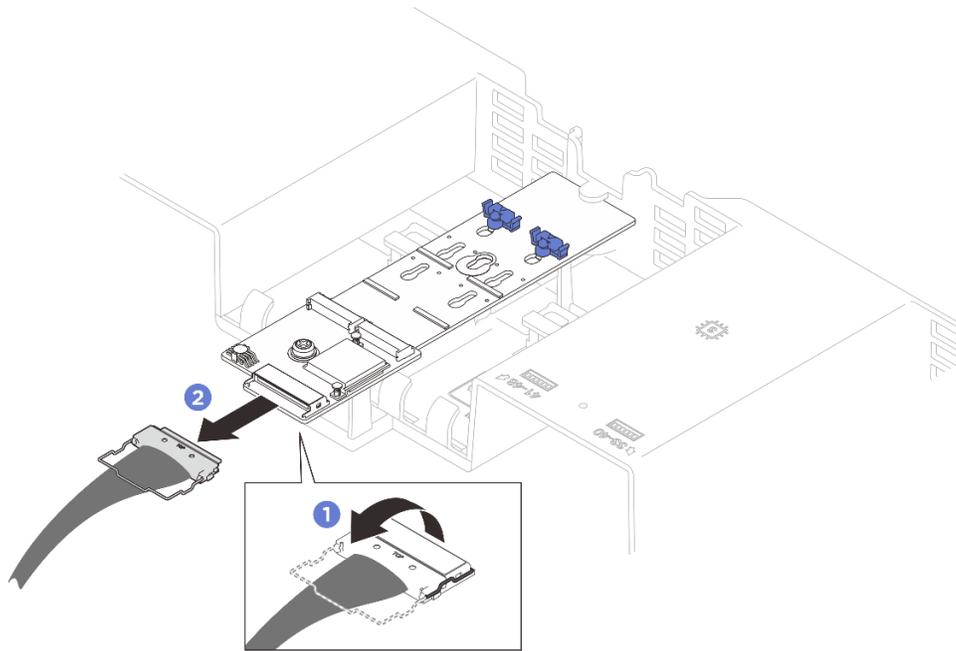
Desconexión de los cables del adaptador de arranque M.2
